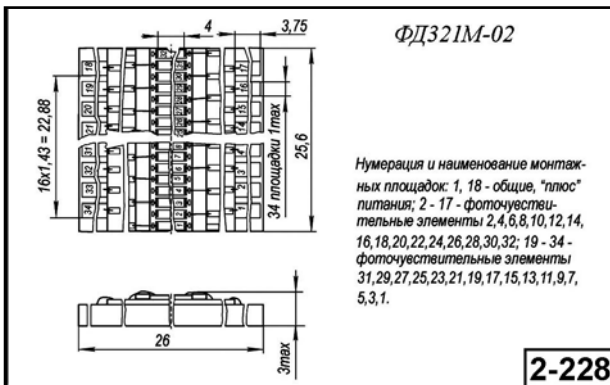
Внешний вид, габаритные размеры кремниевых фотодиодов
